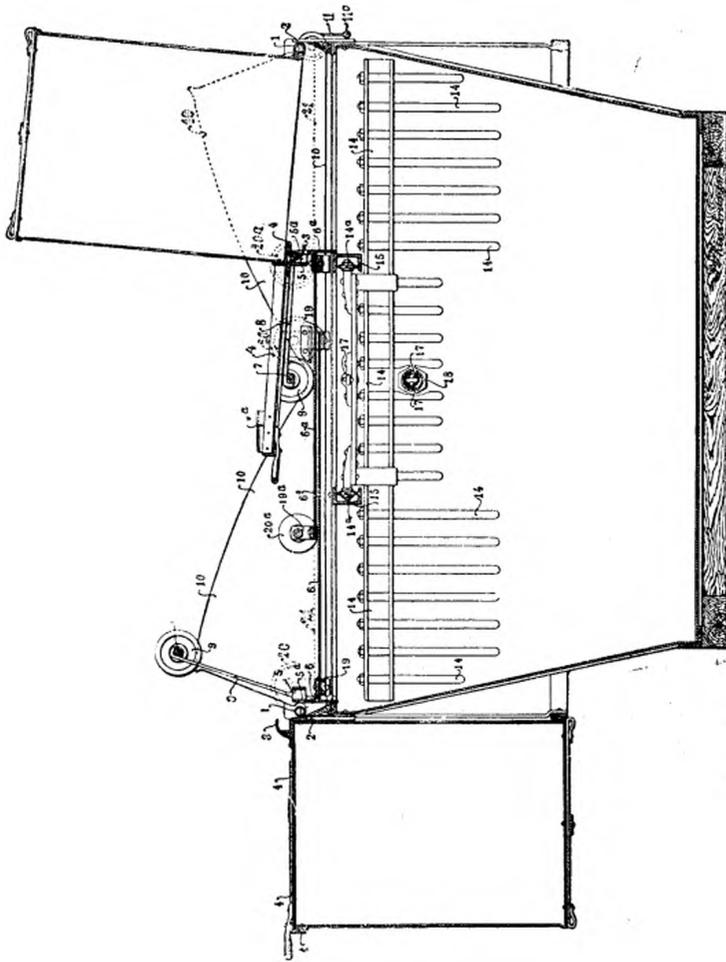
Coupe transversale du caisson de la voiture Kinsbruner.
